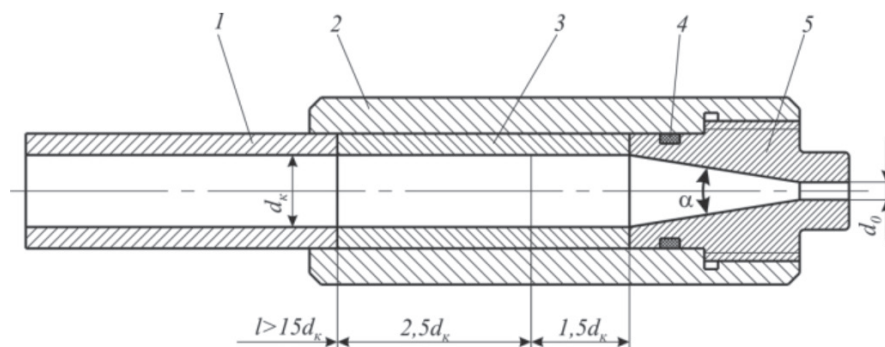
Схема типового полноразмерного струеформирующего устройства:
